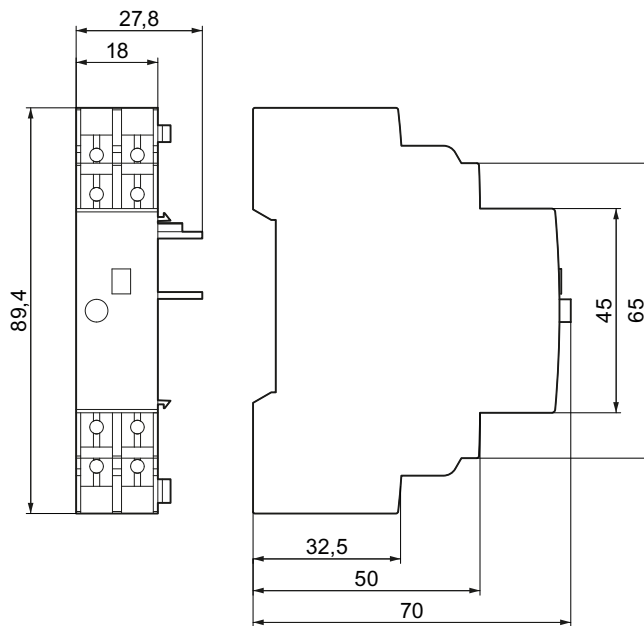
Meldeschalter 3RV2921-4M (Ringkabelschuhanschlusstechnik)
